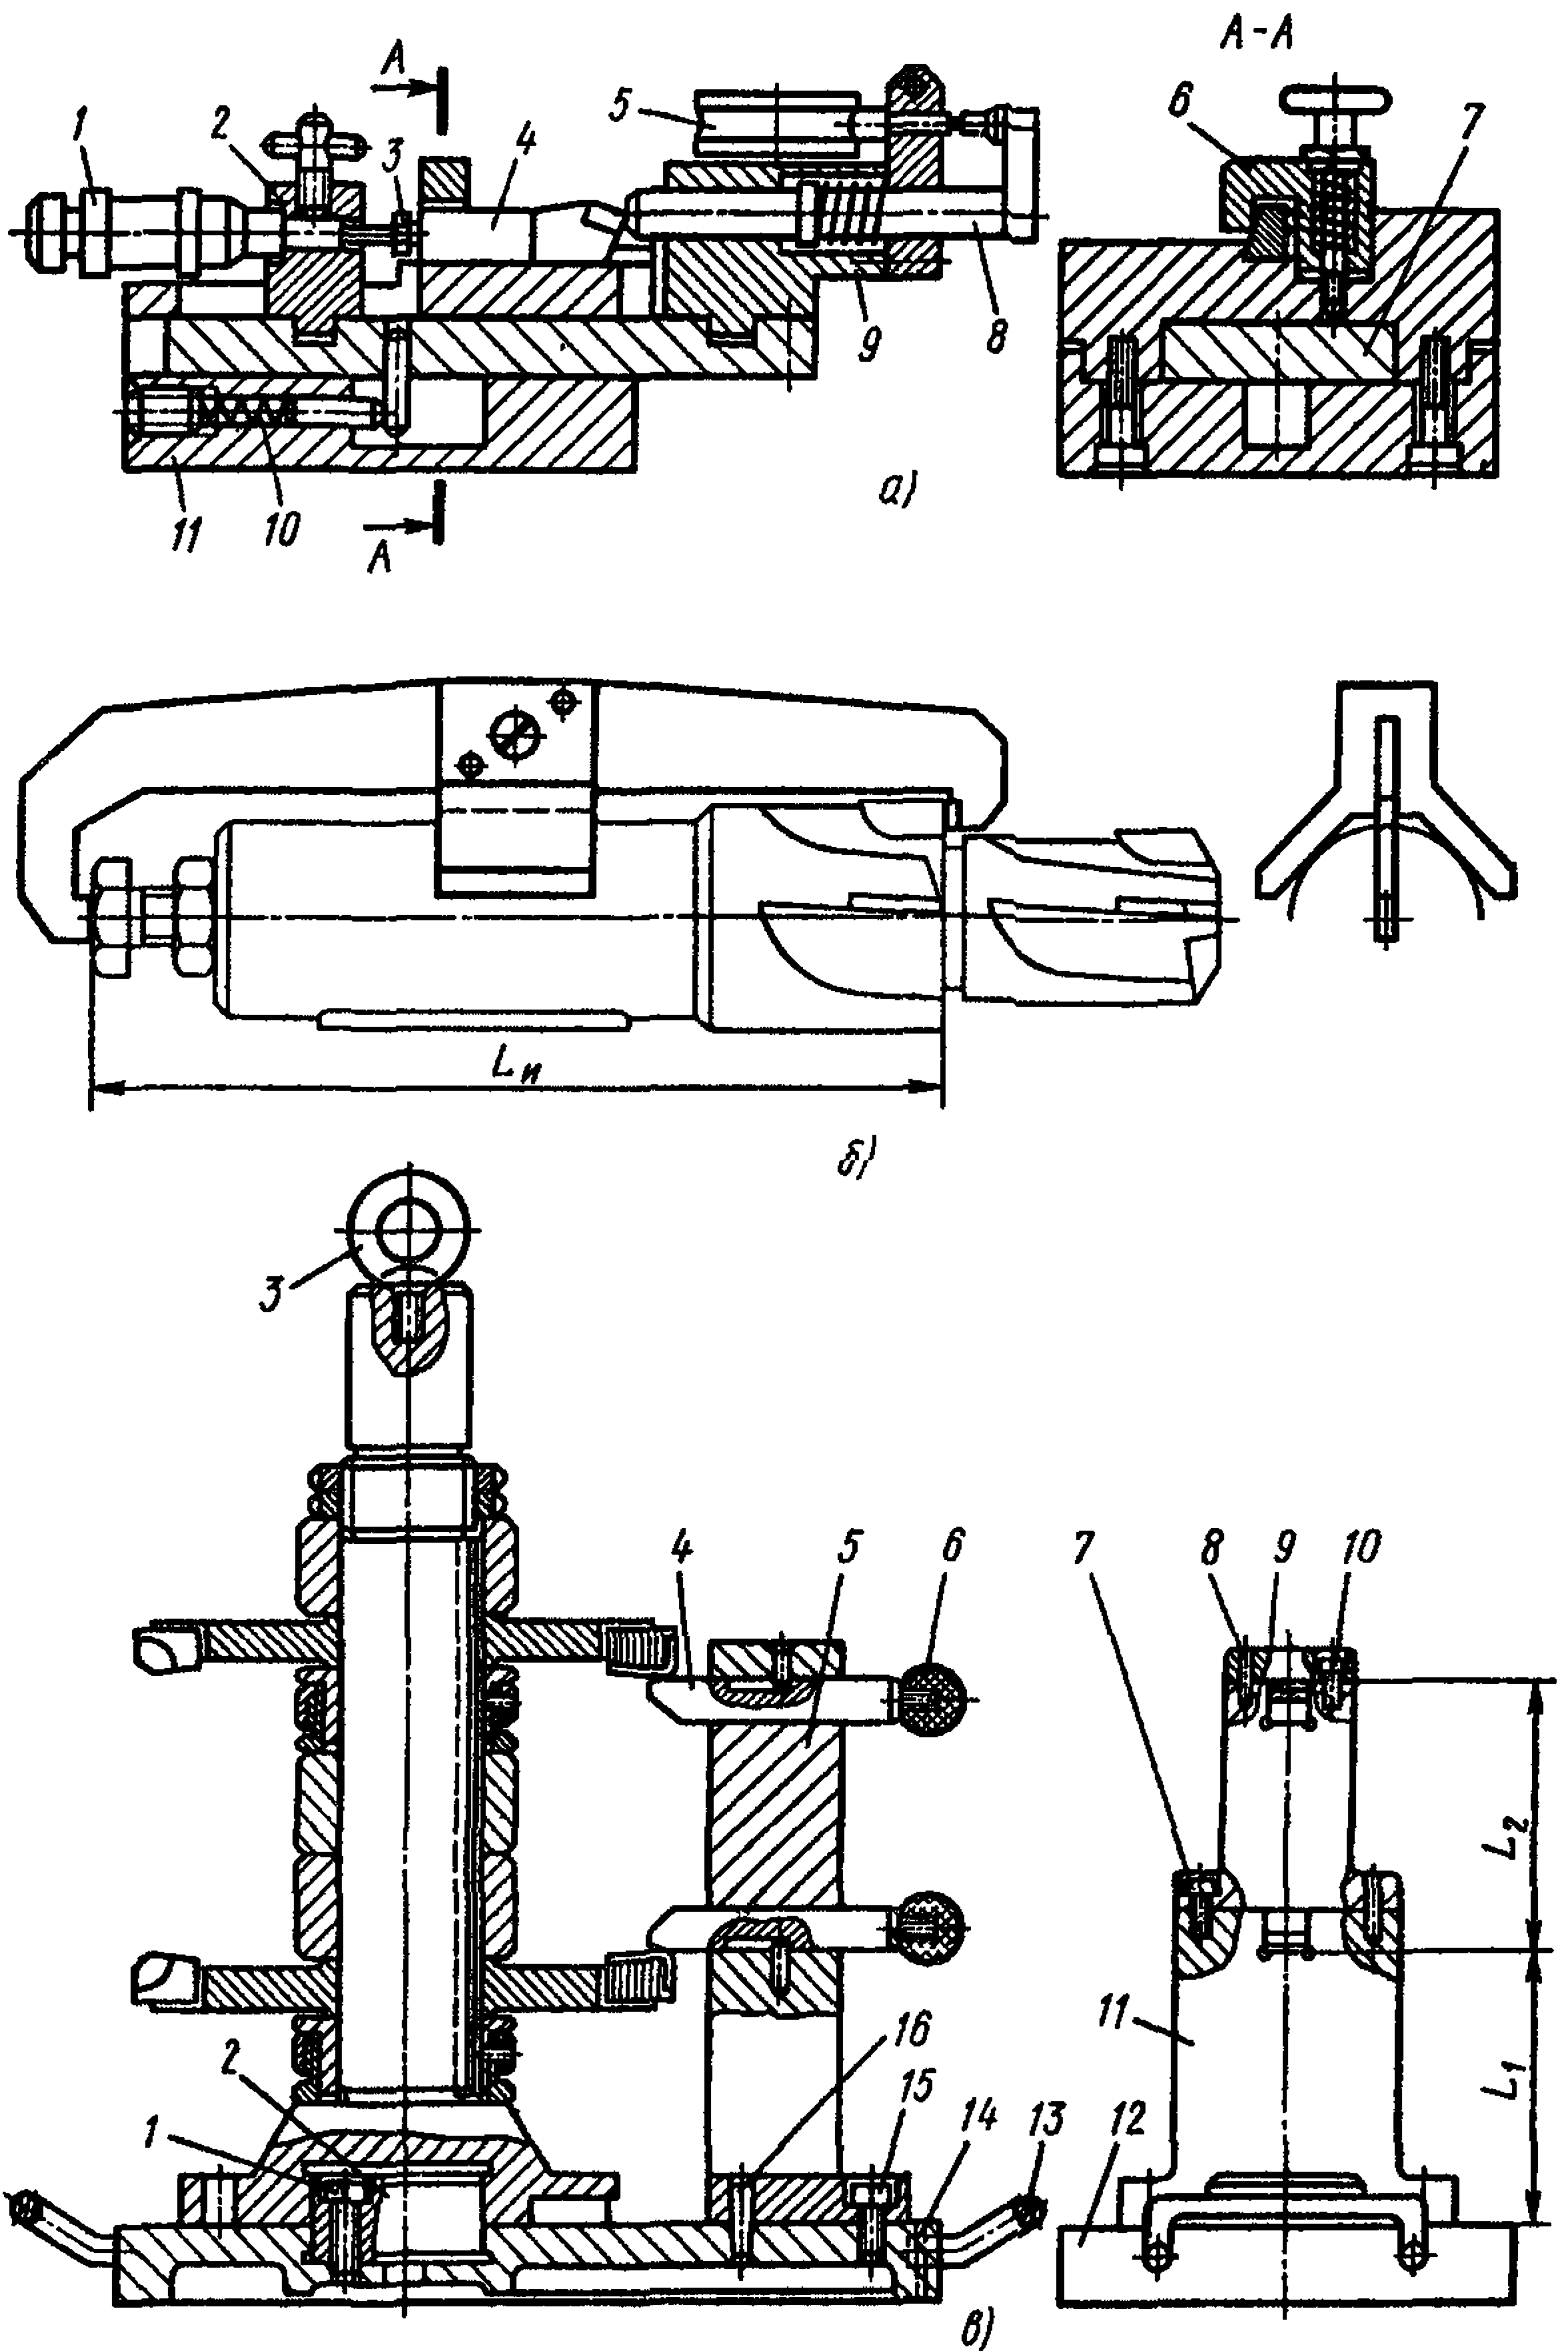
Приспособление для наладки режущих инструментов вне станка:
